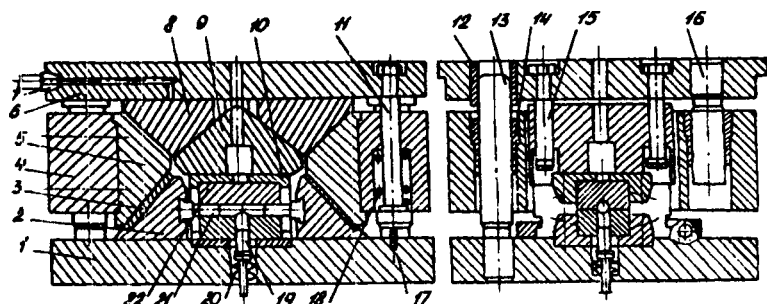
Схема штампа для безоблойной штамповки поковок сложной формы
